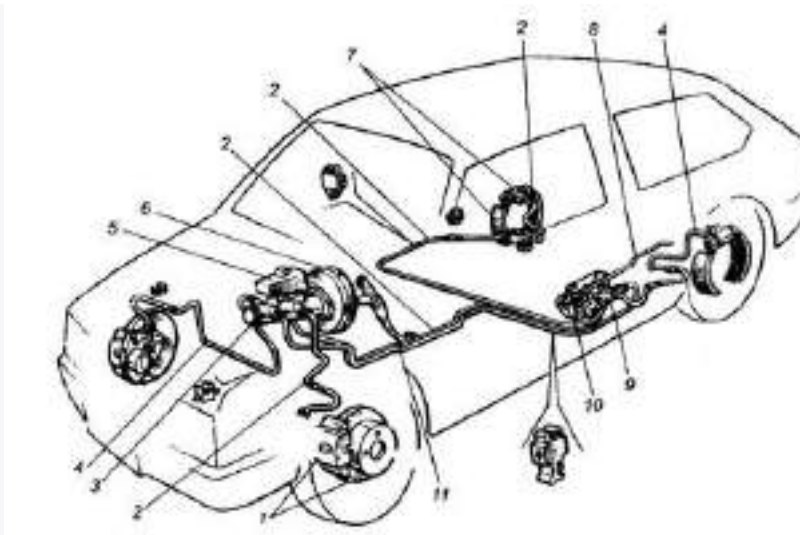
Схема гидропривода тормозных механизмов: 1 — тормозной механизм переднего колеса; 2 — трубопровод контура «левый передний — правый задний тормозные механизмы»; 3 — главный цилиндр гидропривода тормозных механизмов; 4 — трубопровод контура «правый передний — левый задний тормозные механизмы»; 5 — бачок главного цилиндра; 6 — вакуумный усилитель; 7 — тормозной механизм заднего колеса; 8 — упругий рычаг привода регулятора давления; 9 — регулятор давления; 10 — рычаг привода регулятора давления; 11 — педаль тормозной системы.
